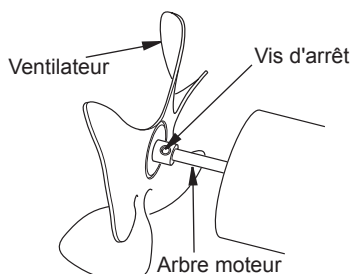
Emplacement du ventilateur, de l'arbre moteur et de la vis d'arrêt
